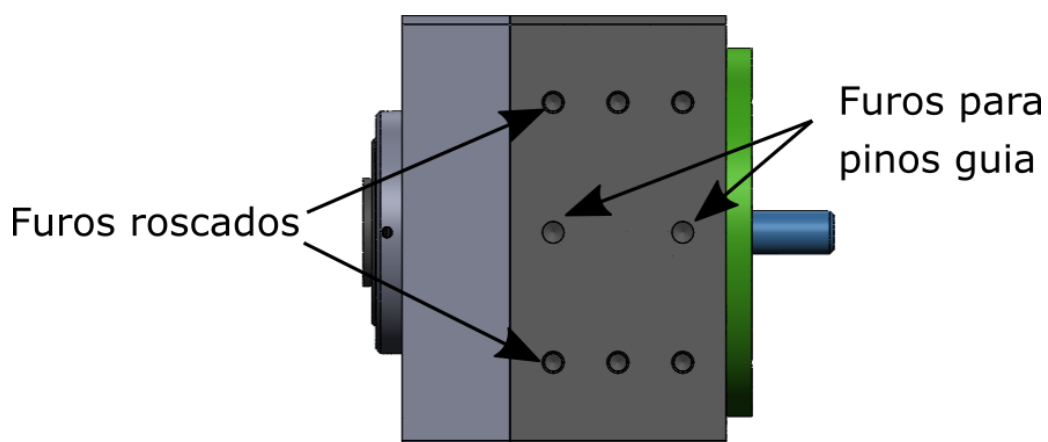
Modelo CAD da montagem do servomotor e redutor
